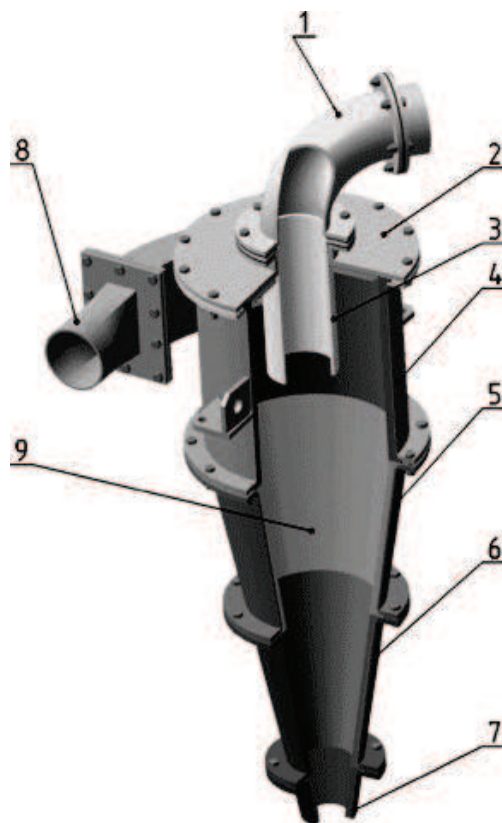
Цилиндрикониический гидроциклон: 1, 3 – верхние сливные патрубки; 2 – крышка; 4 – цилиндрическая часть; 5, 6 – коническая часть; 7 – песковая насадка; 8 – питающий (входной) патрубок; 9 – футеровка внутренней поверхности корпуса
